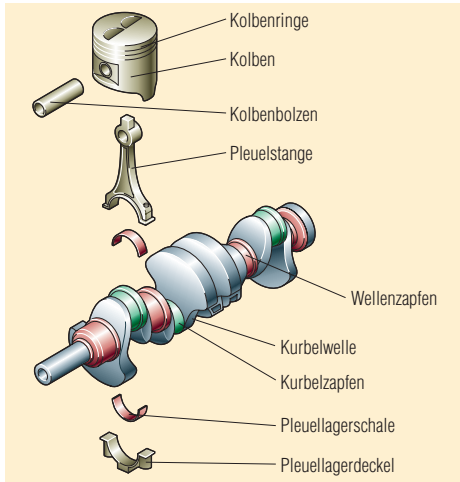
Aufbau Kolben – Kurbelwelle.
